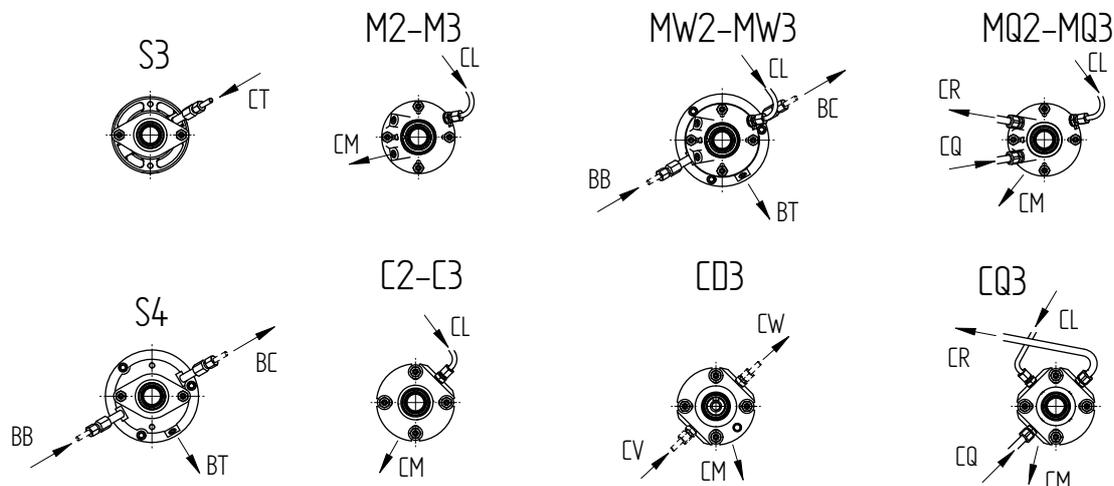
Соединения для групп подшипников 0, 1, 2, 3
